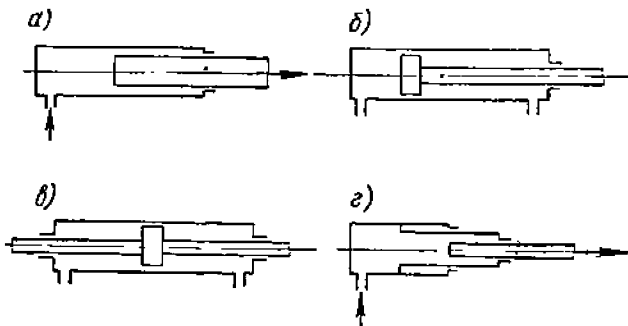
Схемы гидроцилиндров поршневого типа
